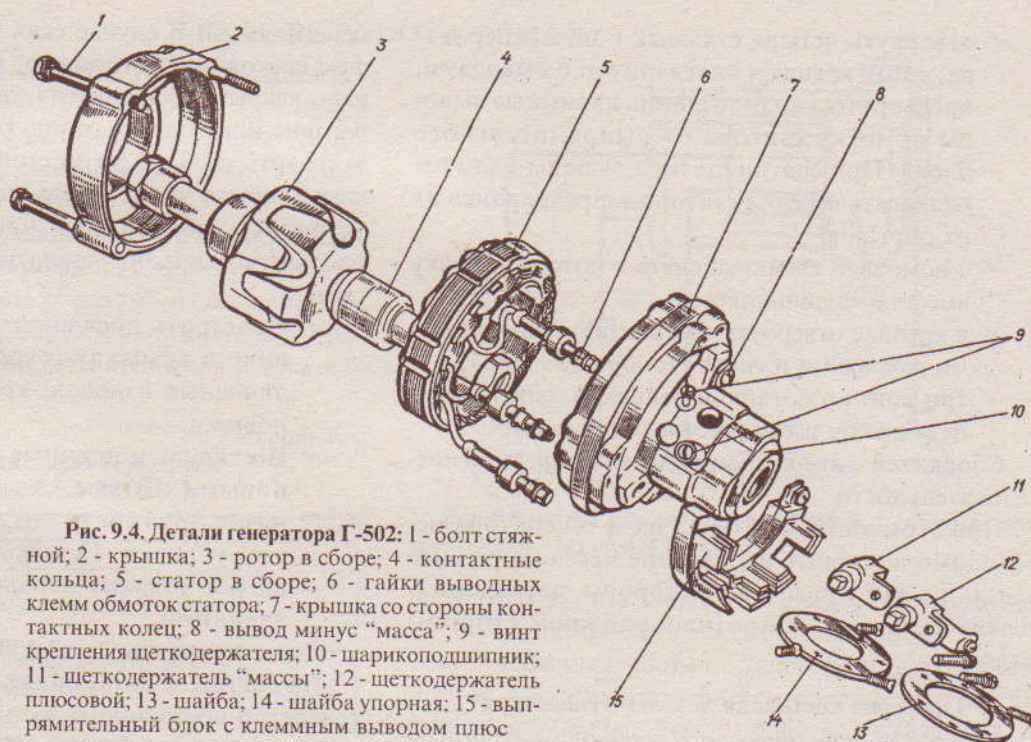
Детали генератора Г-502: 1 - болт стяжной; 2 - крышка; 3 - ротор в сборе; 4 - контактные кольца; 5 - статор в сборе; 6 - гайки выводных клемм обмоток статора; 7 - крышка со стороны контактных колец; 8 - вывод минус "масса"; 9 - винт крепления щеткодержателя; 10 - шарикоподшипник; 11 - щеткодержатель "массы"; 12 - щеткодержатель плюсовой; 13 - шайба; 14 - шайба упорная; 15 - выпрямительный блок с клеммным выводом плюс
